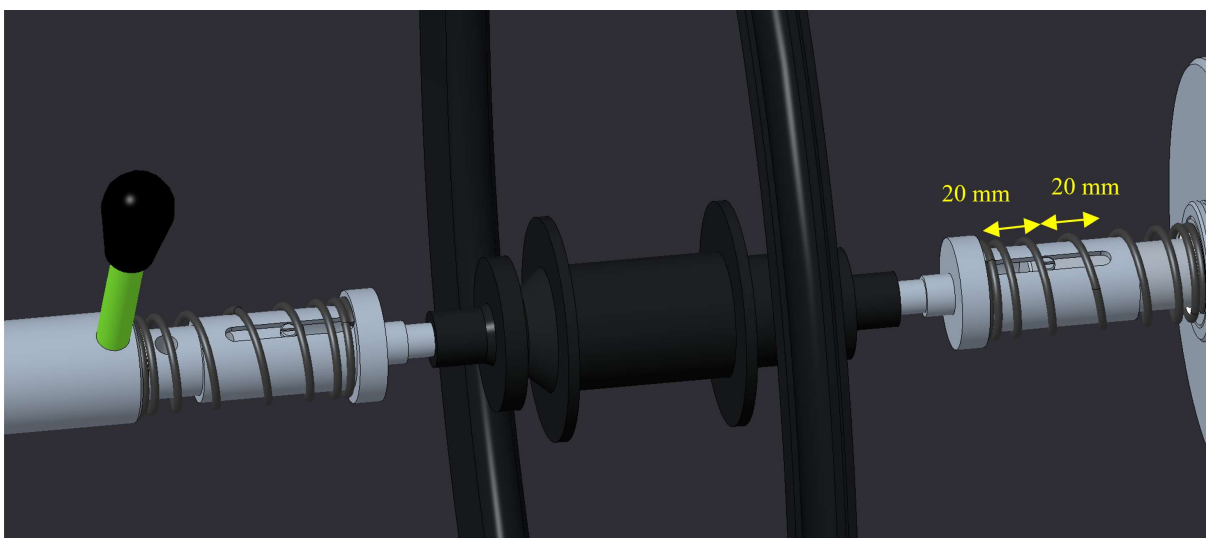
Demonstração do posicionamento proposto do cubo para montagem
